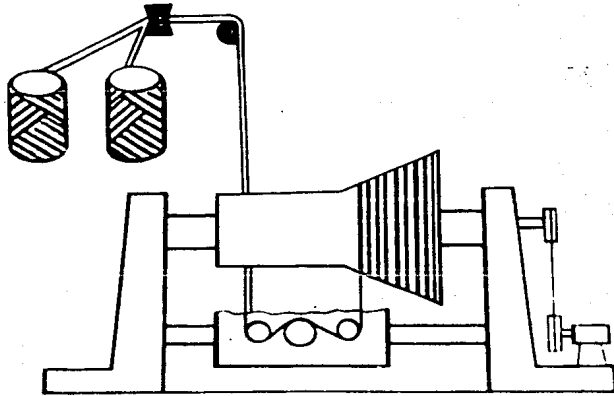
MOLDEO POR EMOBINADO DE FILAMENTOS
